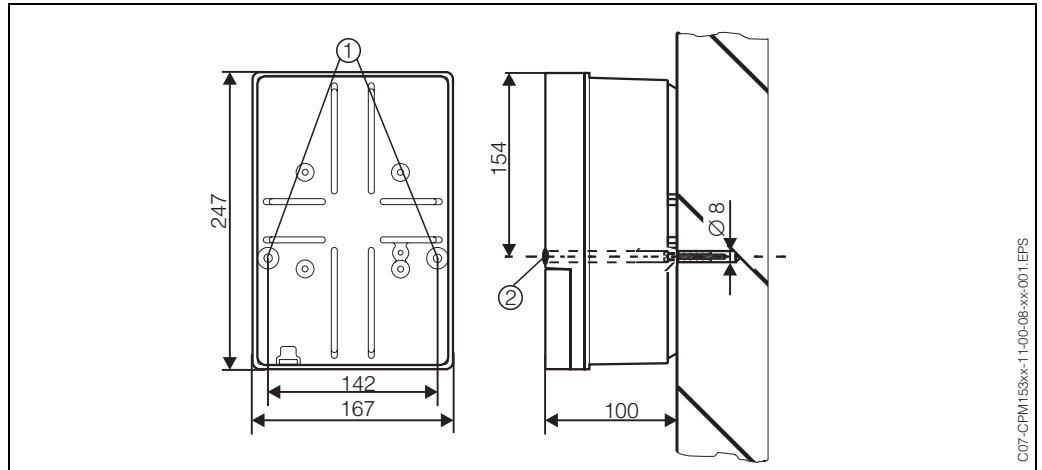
Maße für die Wandmontage: Befestigungsschraube: \varnothing 6 mm, Dübel: \varnothing 8 mm
